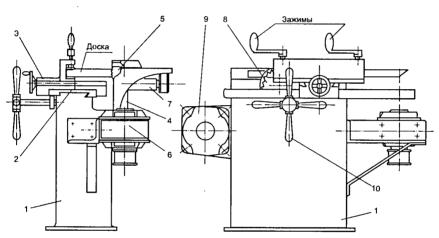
Общий вид станка для изготовления клиньев: 1 — литая станина, 2 — салазки горизонтального хода, 3 — салазки поперечного хода, 4 — вал фасонной фрезы, 5 — фасонная фреза, 6 и 9 — электродвигатель, 7 — вал дисковой пилы, 8 — дисковая пила, 10 — штурвал
